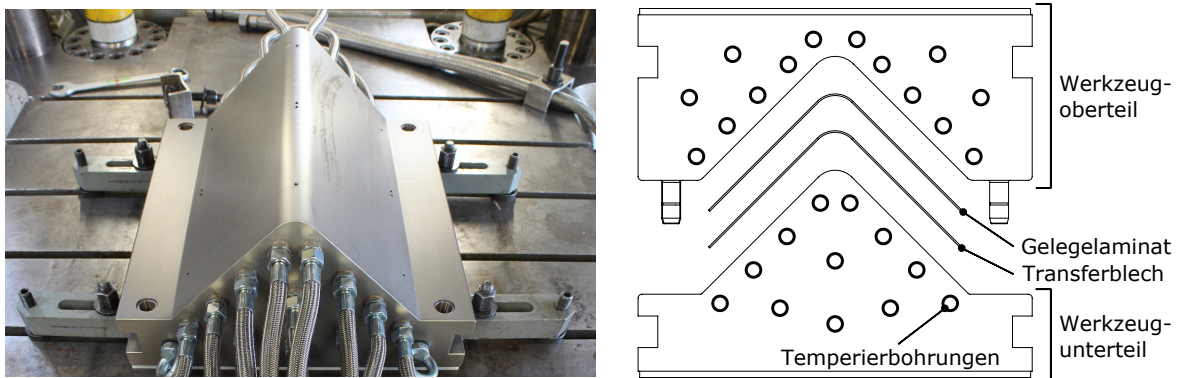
Explosionsansicht von Presswerkzeug, Transferblech und Versuchskörper in PS2
